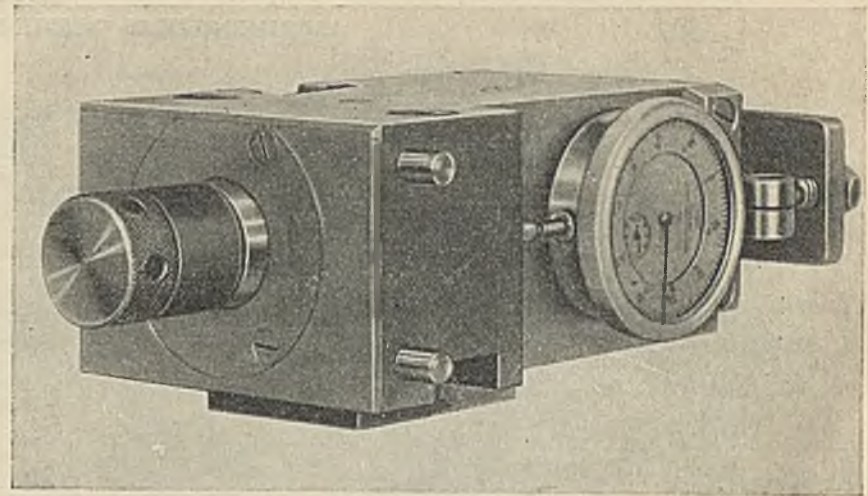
Общий вид динамометра для металлорежущих станков.
